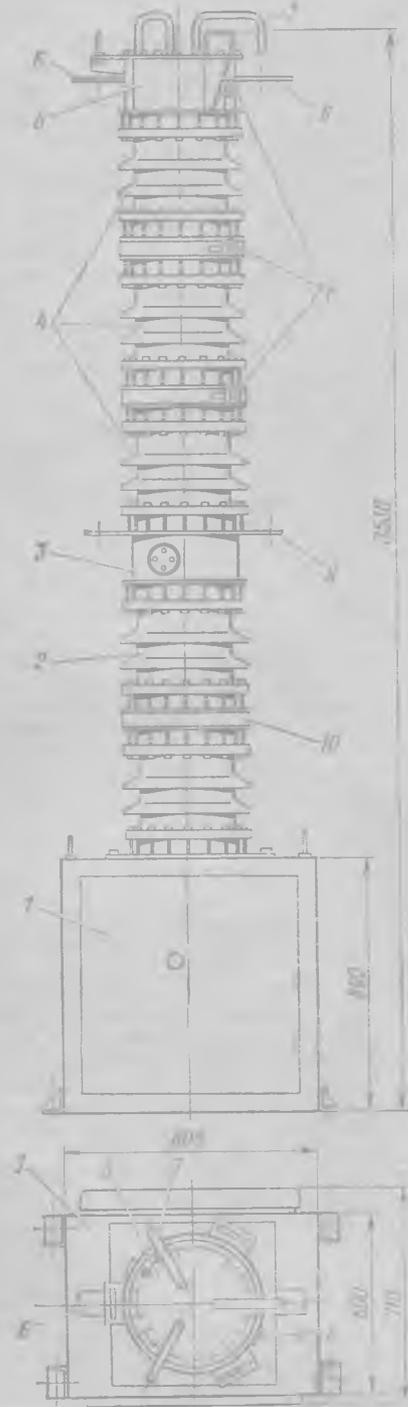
Установочный чертеж вакуумного выключателя ВВФ-27,5
